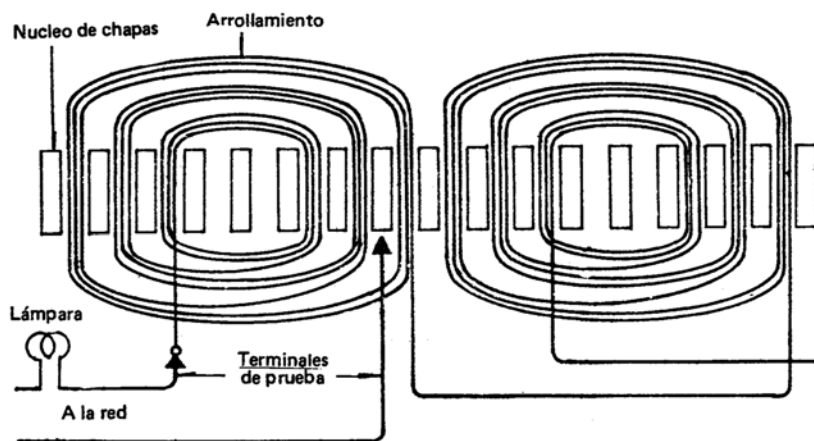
PARA DETERMINAR CONTACTO A MASA EN EL ARROLLAMIENTO CON UN TERMINAL DE LA LÁMPARA SERIE EN CONTACTO CON EL ARROLLAMIENTO Y EL OTRO CON LA CHAPA DEL ESTATOR. SI SE ENCIENDE, HAY CONTACTO A MASA.
